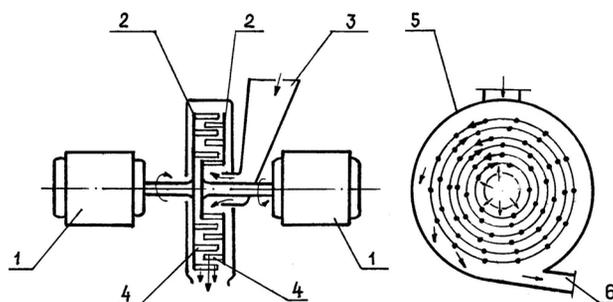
Схема дезинтегратора: 1 – электродвигатель; 2 – вращающийся диск; 3 – загрузочная воронка; 4 – пальцы; 5 – корпус; 6 – патрубок отвода.
